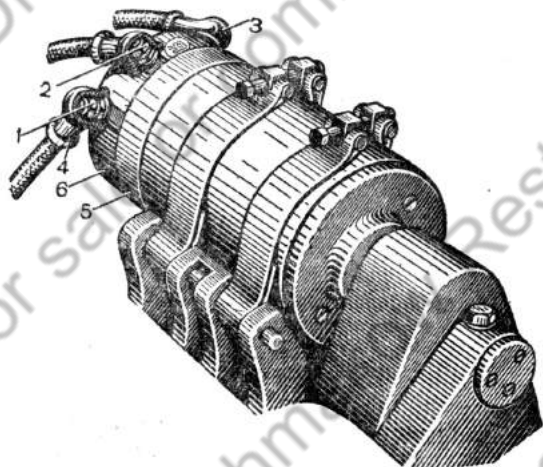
Мотор поворота башни МВ-20К (общий вид): 1 — клеммовый болт обмотки возбуждения; 2 — клеммовый болт обмотки якоря; 3 — клеммовый болт обмотки возбуждения с резиновым наконечником; 4 — рывковый наконечник; 5 — защитная лента; 6 — кожух
